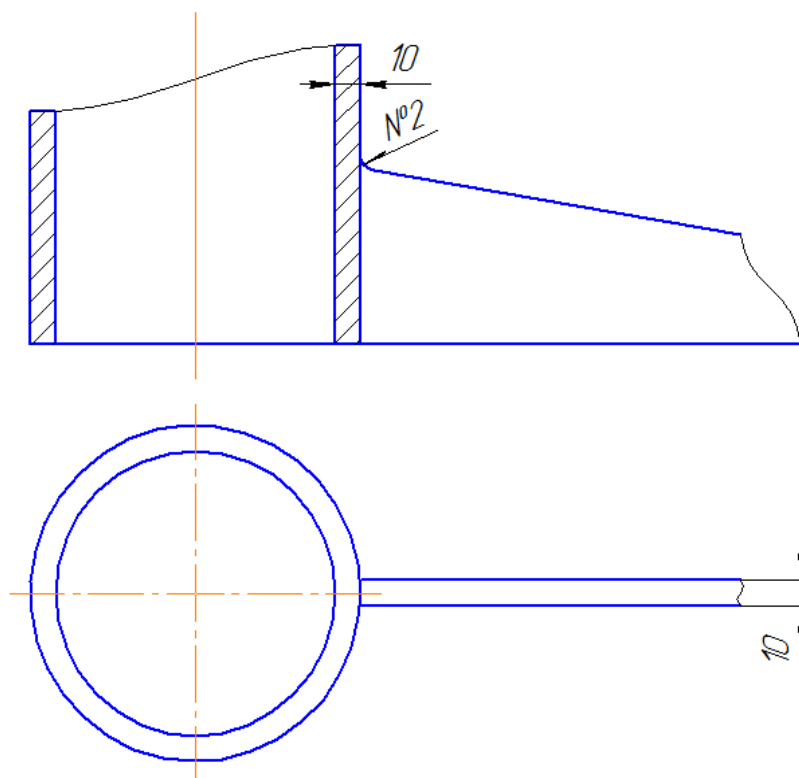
Эскиз сварного соединения наружная труба – ножки
